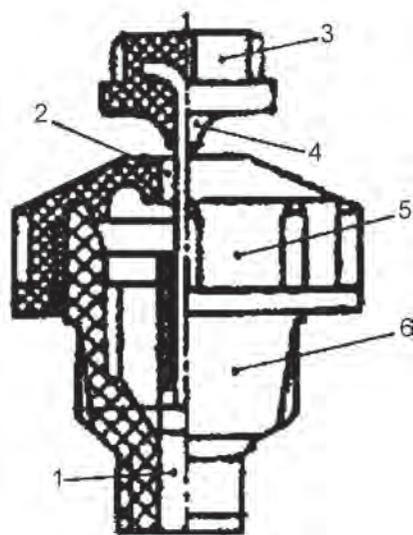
Насадка стержневого типа: 1 – входное отверстие; 2 – выходное отверстие (сопло); 3 – гайка-регулятор; 4 – дефлектор; 5 – крышка; 6 – корпус
